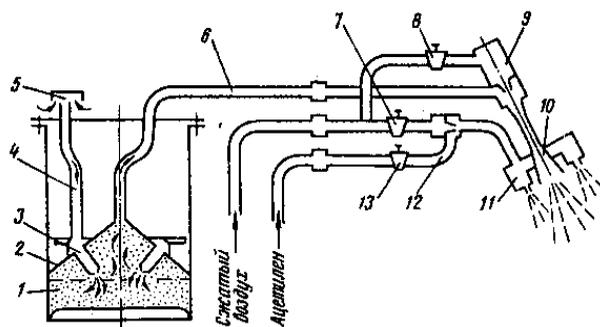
Схема установки для газопламенного напыления полимеров:
